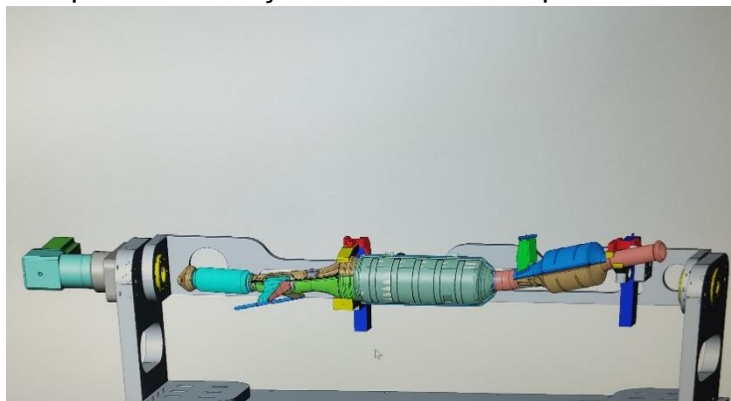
Início do desenvolvimento em CAD da estação de soldadura
